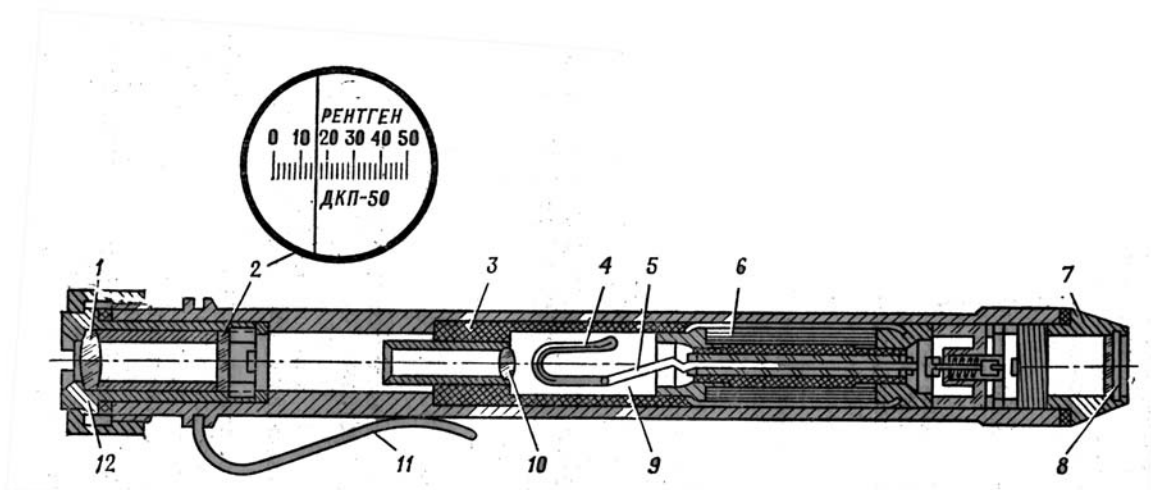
ДКП-50: 1 – окуляр; 2 – шкала; 3 – корпус; 4 – визирная нить; 5 – внутренний электрод; 6 – конденсатор; упорная втулка; 7 – защитная оправа; 8 – стекло; 9 – ионизационная камера; 10 – объектив; 11 – держатель; 12 – верхняя пробка
